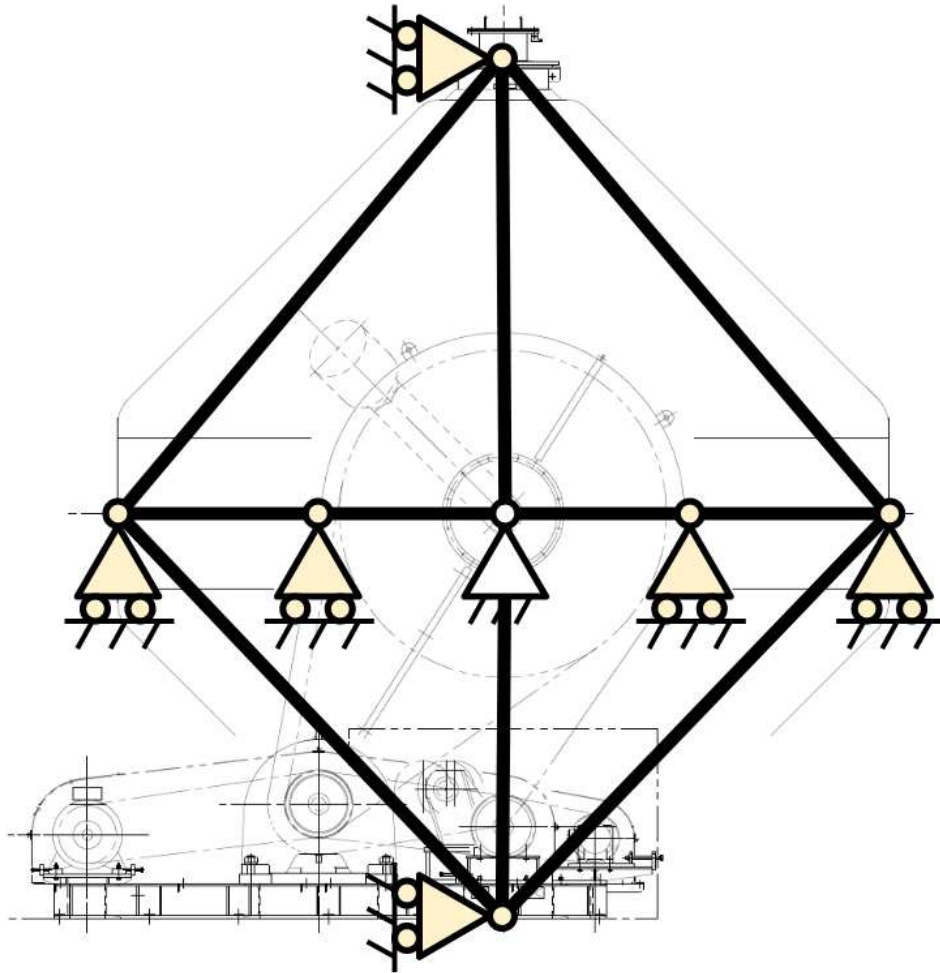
Posibles restricciones (apoyos en amarillo) que debe efectuar el enclavamiento.
